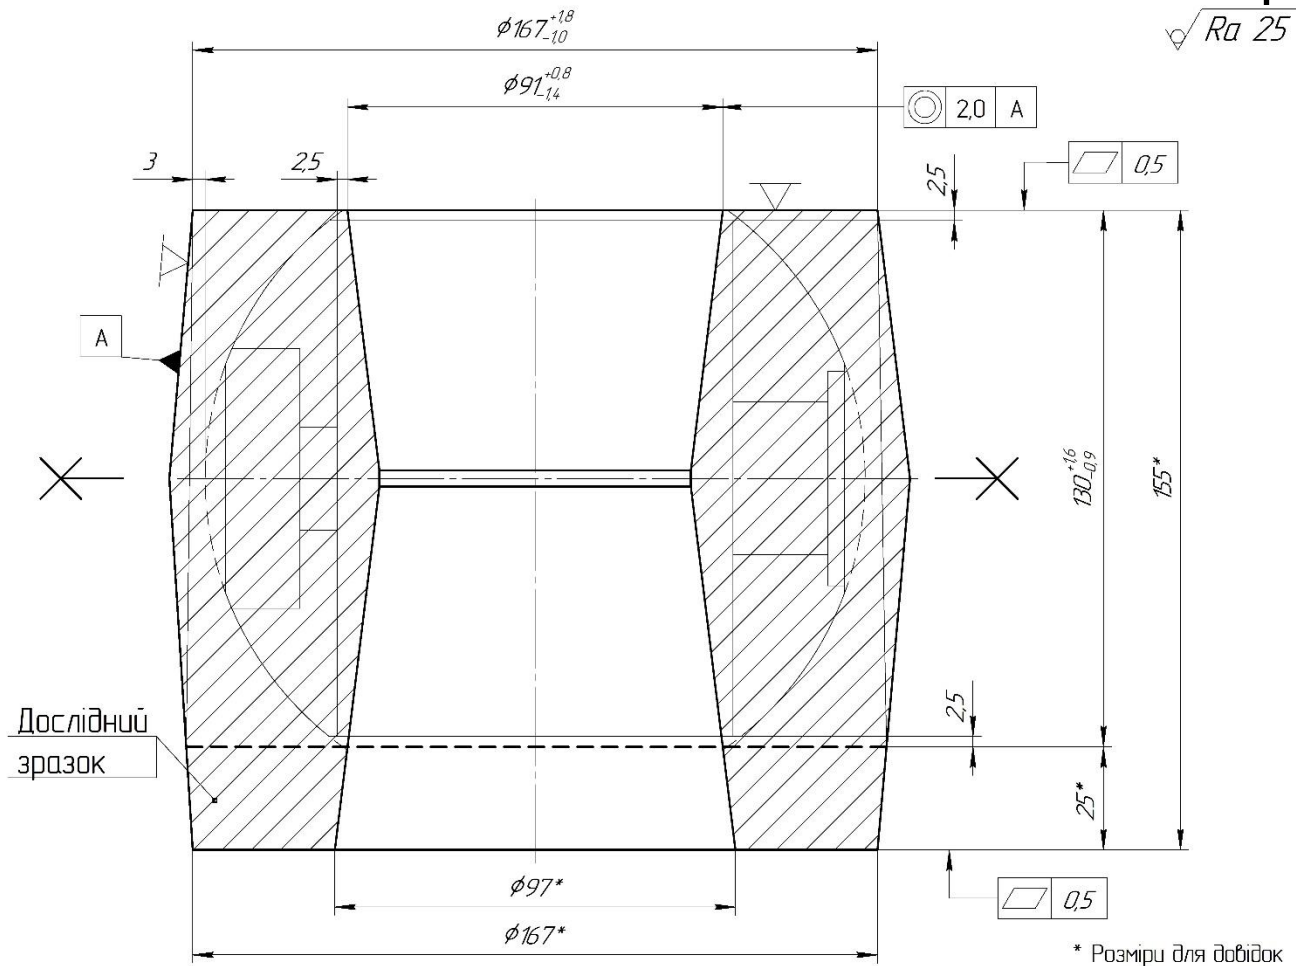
Ескіз заготовки, яка виготовлена на КГШП
